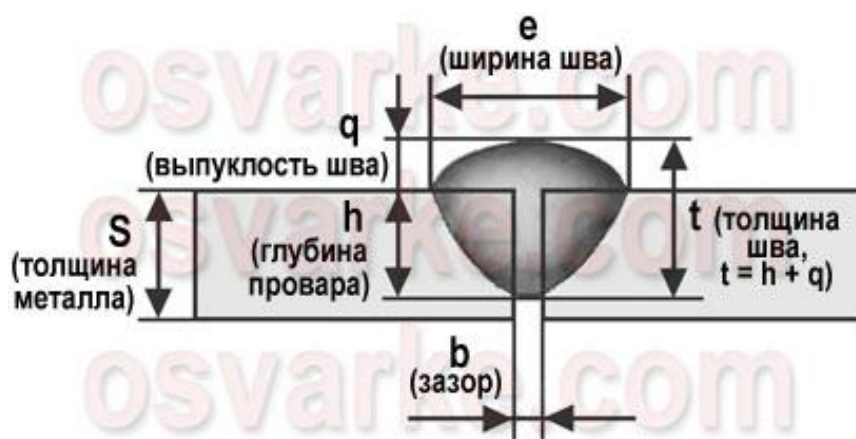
а. Геометрические параметры сварного шва.
